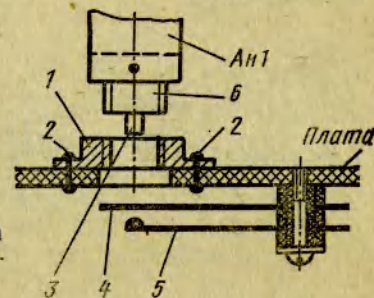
Эскиз конструкции узла крепления антенны и выключателя В2
